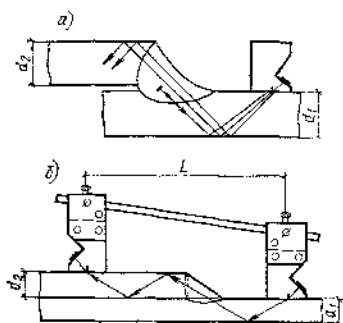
Контроль нахлесточных сварных соединений по совмещенной схеме (а) и зеркально-тенивым способом по раздельной схеме (б)
